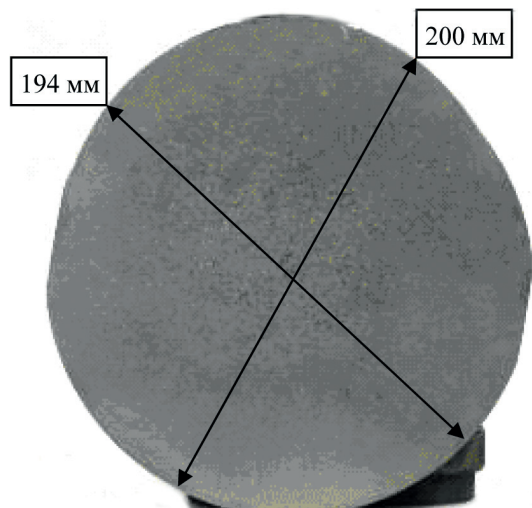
Макроструктура поперечного сечения непрерывнолитой заготовки диаметром 200 мм
